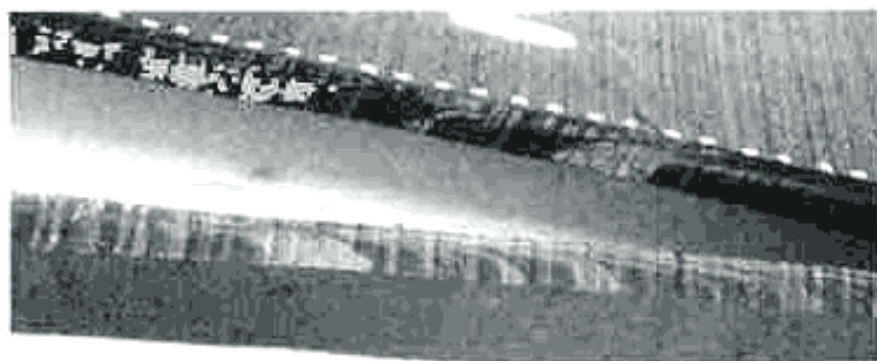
Образец ПЭ с гладкой поверхностью разрушения
